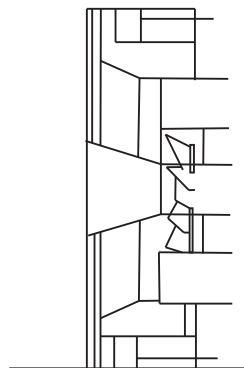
Установка горелки в корпусе котла П-57 блока 500 МВт
